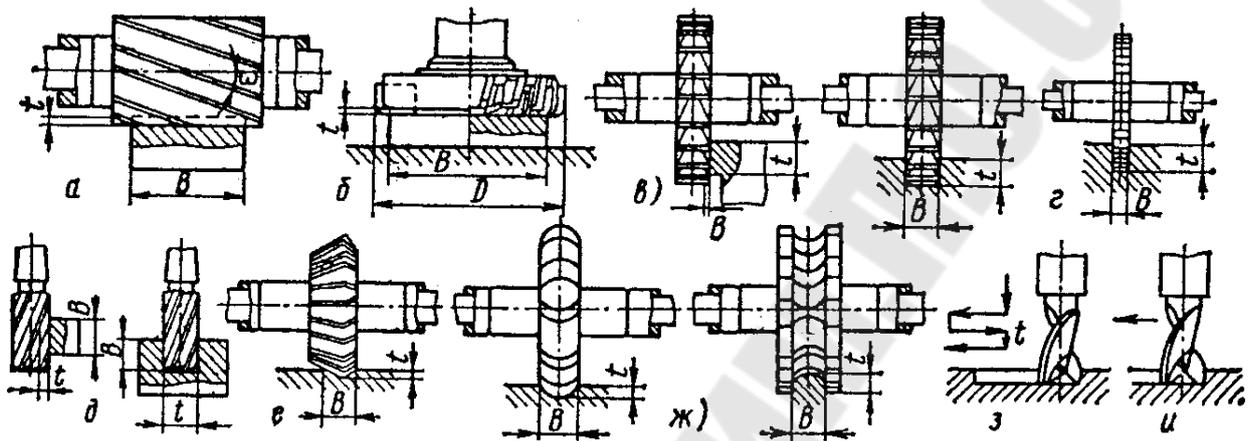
Примеры обработок на фрезерных станках различными фрезами
